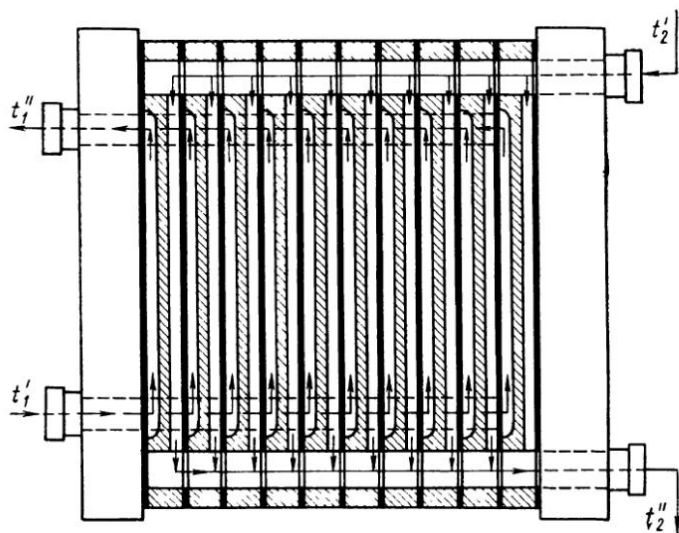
Схема пластинчатого теплообменника с фрезерованными бронзовыми пластинами
